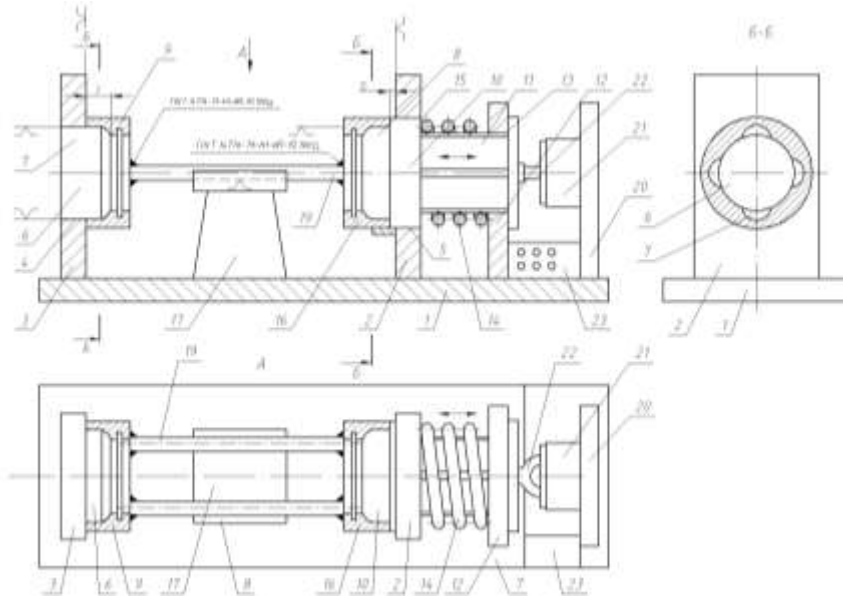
Пристрій для зварювання секцій гіперболічного шнека
